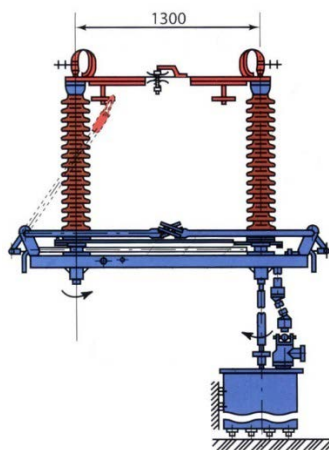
Внешний вид разъединителя марки РЛНД-2-35-600
